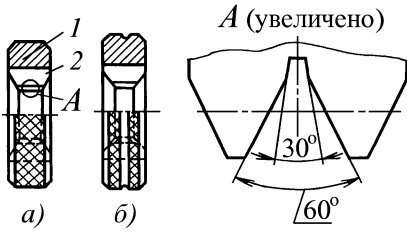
Резьбовое калибровое проходное (а) и непроходное (б) кольцо из твердого сплава:
